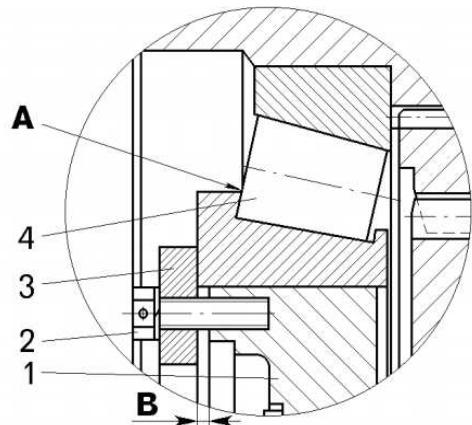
Проверка зазора: 1 – корпус редуктора; 2 – болт; 3 – кольцо упорное; 4 – подшипник; А – место установки щупа; В – зазор
